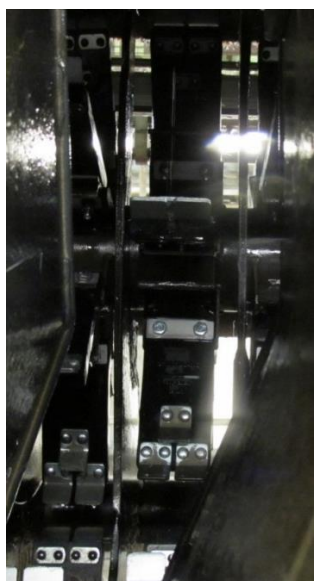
viser "bagsiden" af tromle og lapper. Foto er taget fra pladesiden.
